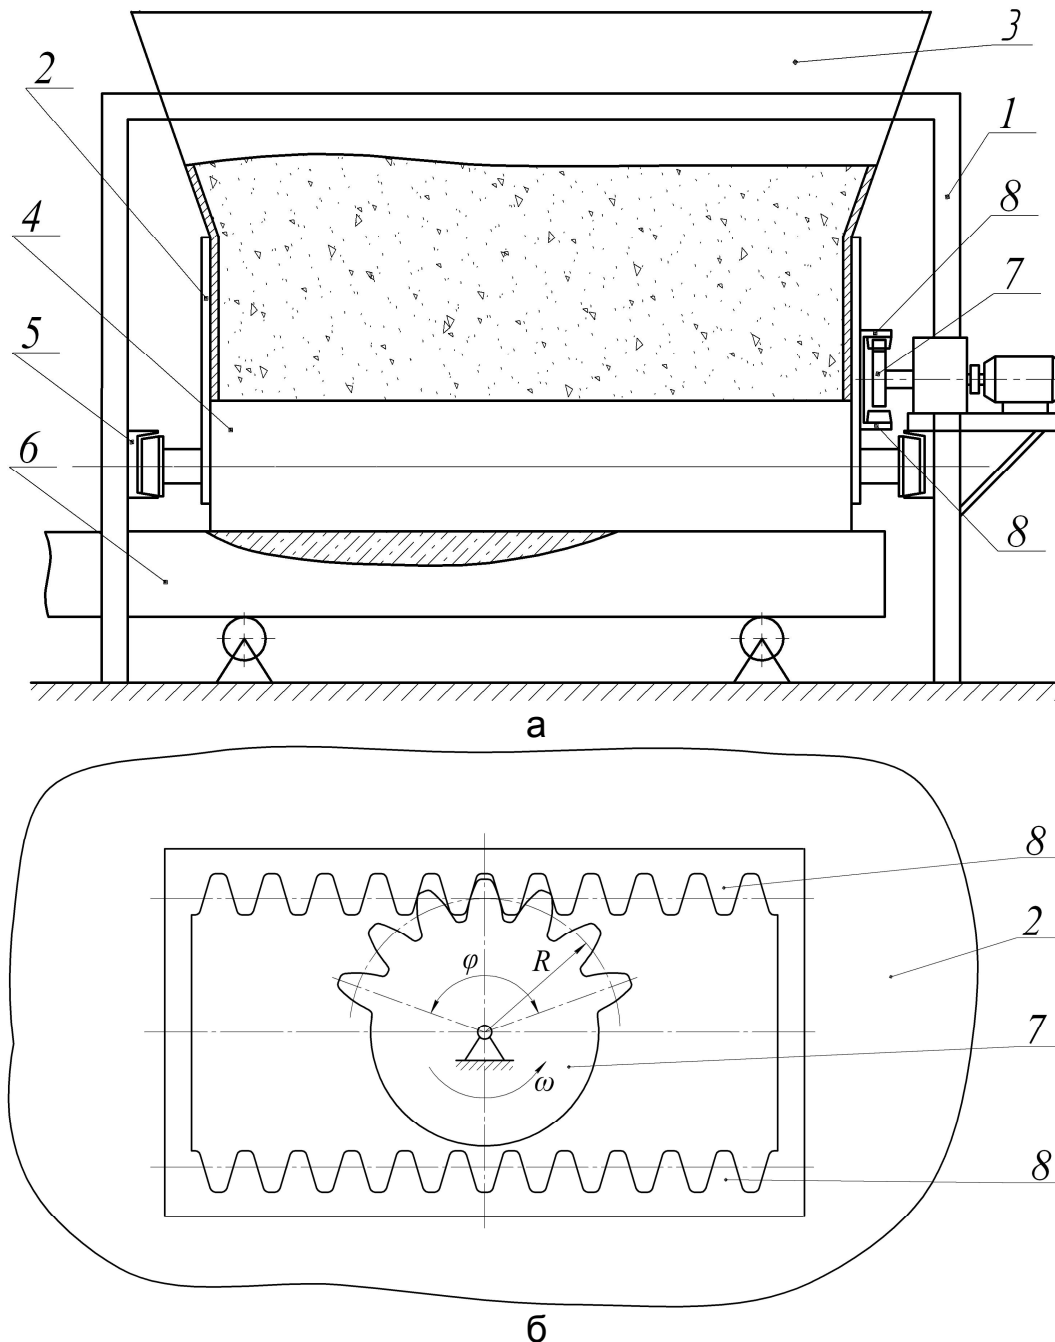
Роликова формувальна установка з приводом від зубчастого сектора (а) та схема приводного механізму (б)
